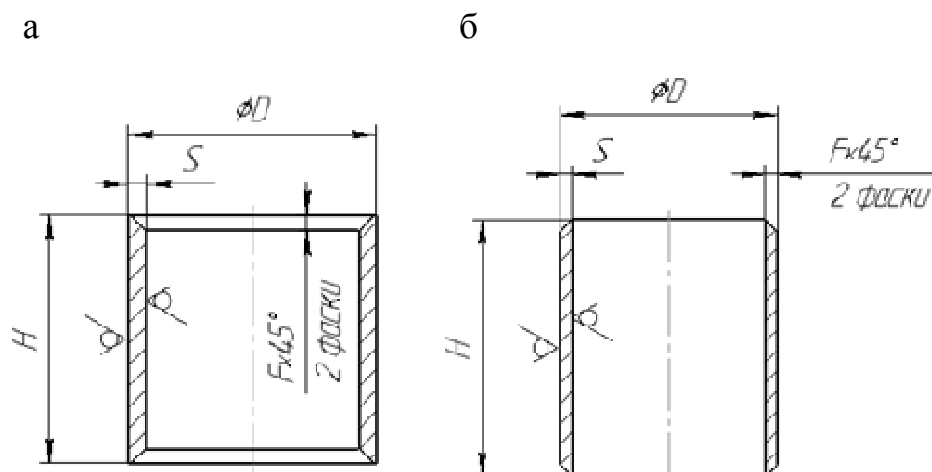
Заготовки под обжим: заготовка под сферическую оболочку (а), заготовка под внутренний патрубок (б)
